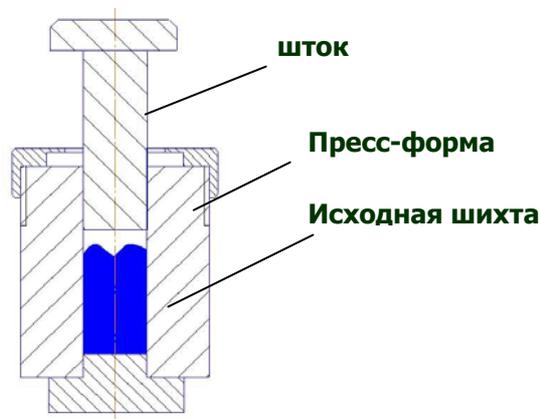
Схема пресс-формы для одностороннего прессования заготовок.
